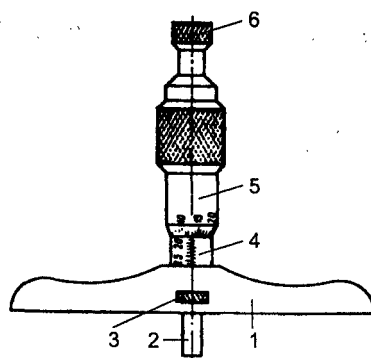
Микрометрический глубиномер: 1 — корпус; 2 — микрометрический винт; 3 — стопор; 4 — стержень; 5 — барабан; 6 — храповой механизм
